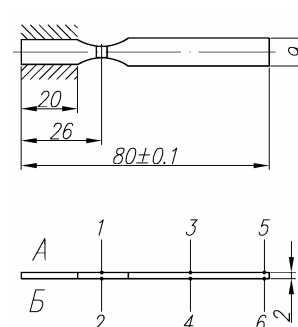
Эскиз образца для испытаний на усталость и схема расположения термопар
